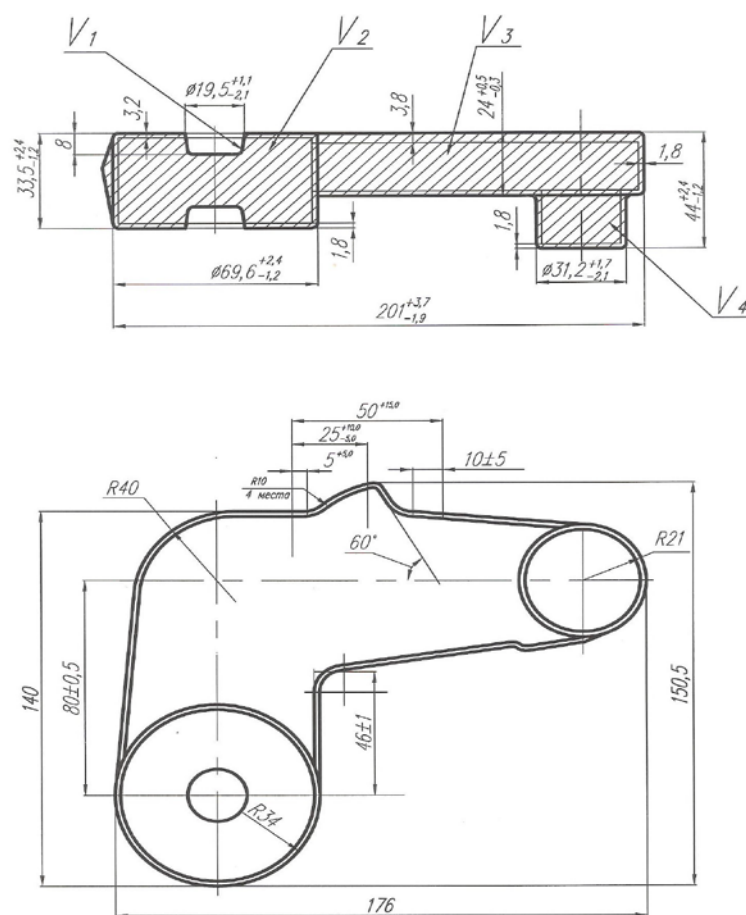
Эскиз заготовки – штамповки детали «Кривошип»
